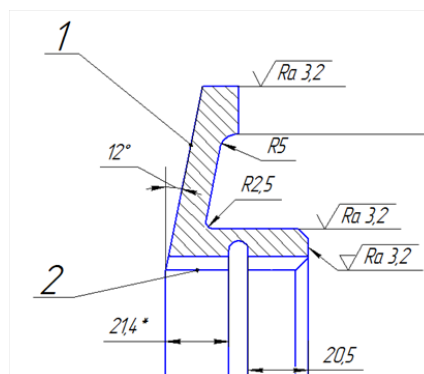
Расположение поверхностей обработки шкива: 1 – поверхность взаимодействия с ремнем вариатора; 2 – шлицевое соединение
